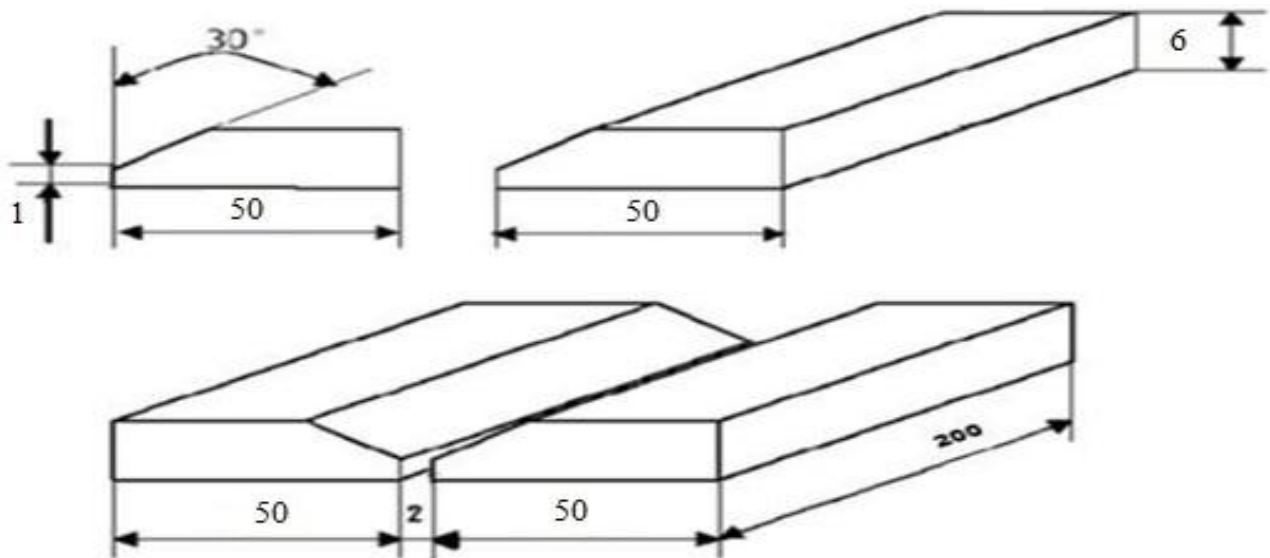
Schéma de principe pour l'assemblage par soudage MIG des deux métaux de base sous forme de tôles fortes de 6 mm d'épaisseur.
